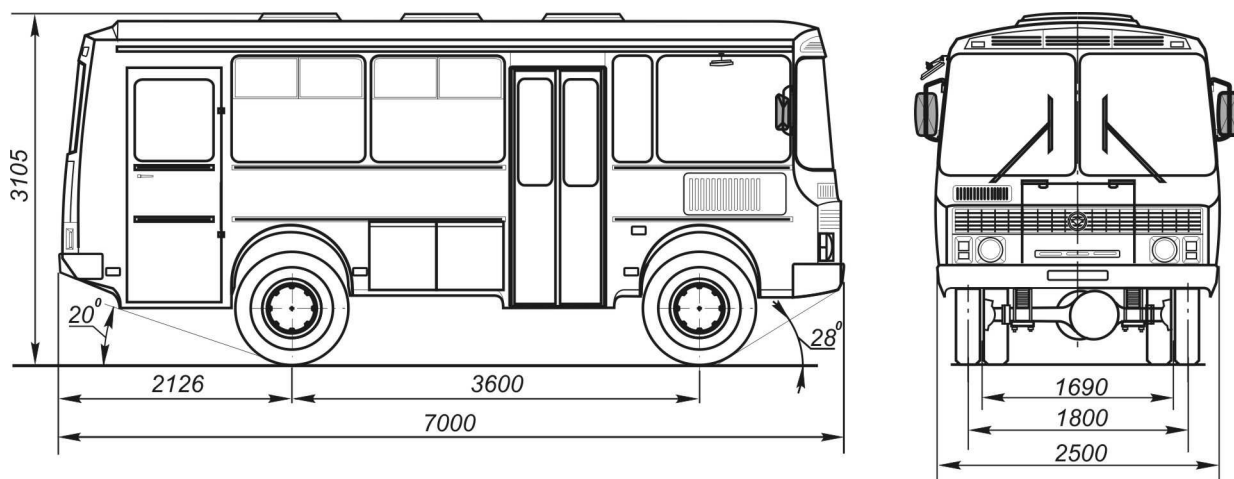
Габаритные размеры автобуса ПАЗ-3206-110
